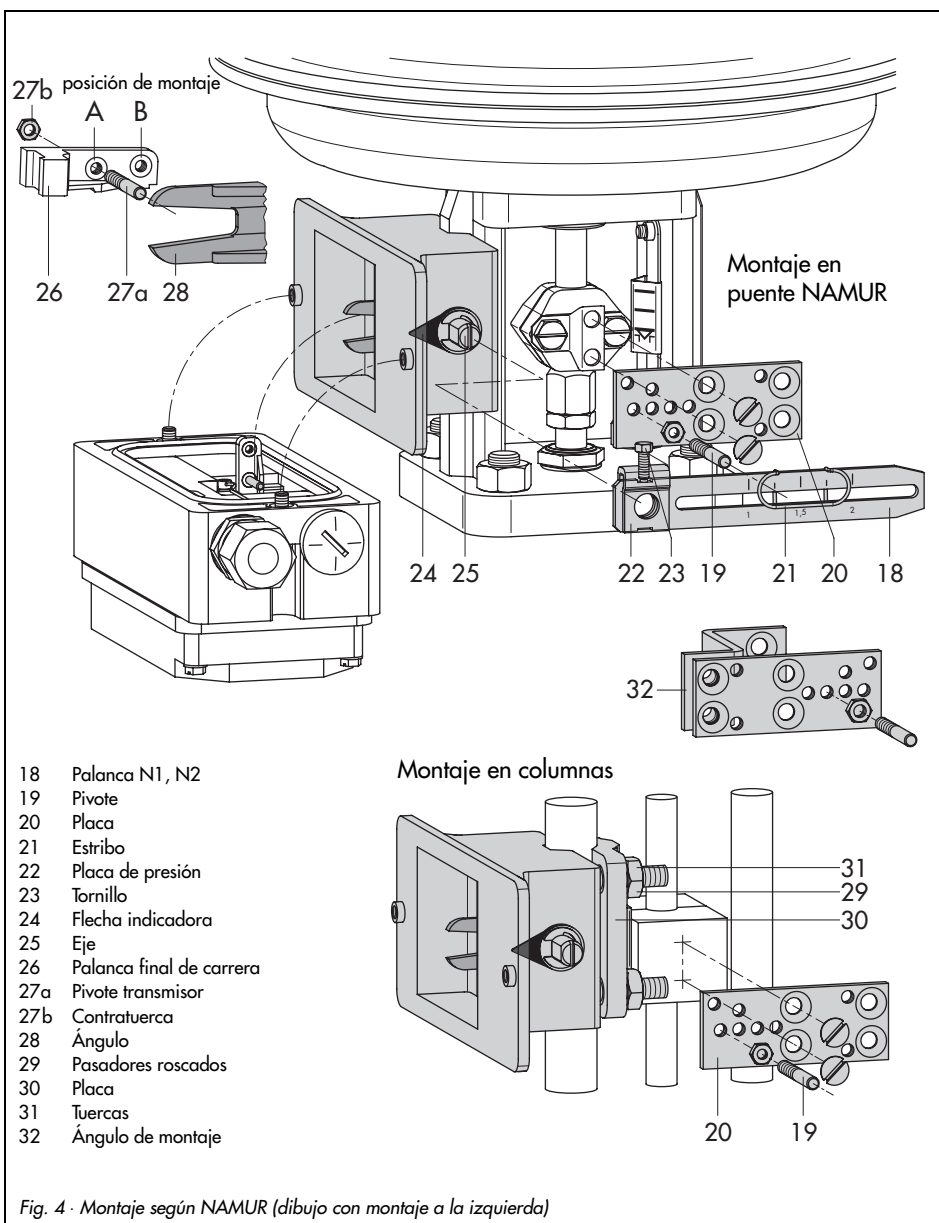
· Montaje según NAMUR (dibujo con montaje a la izquierda)
